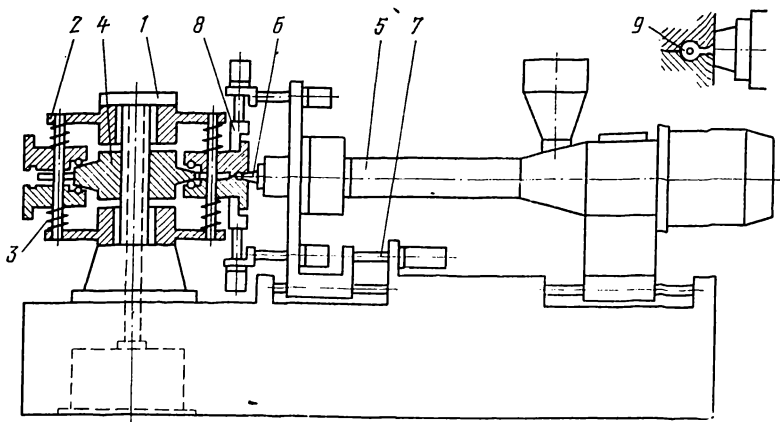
Агрегат для непрерывной отливки полиэтиленовых шайб на внутренний проводник коаксиальной пары.
